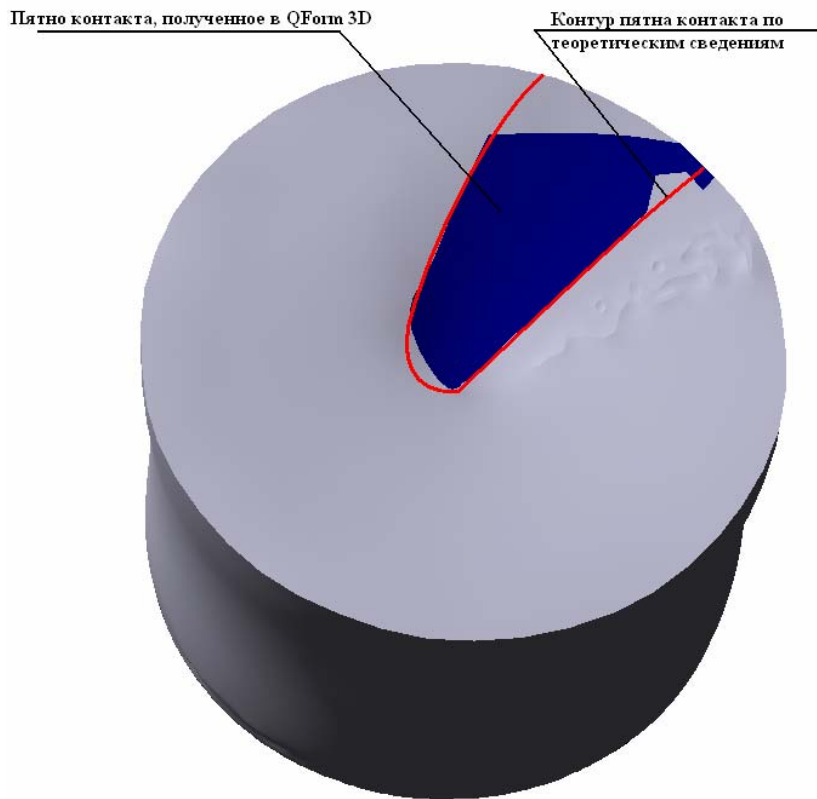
Изображение пятна контакта на верхней торцевой поверхности заготовки
